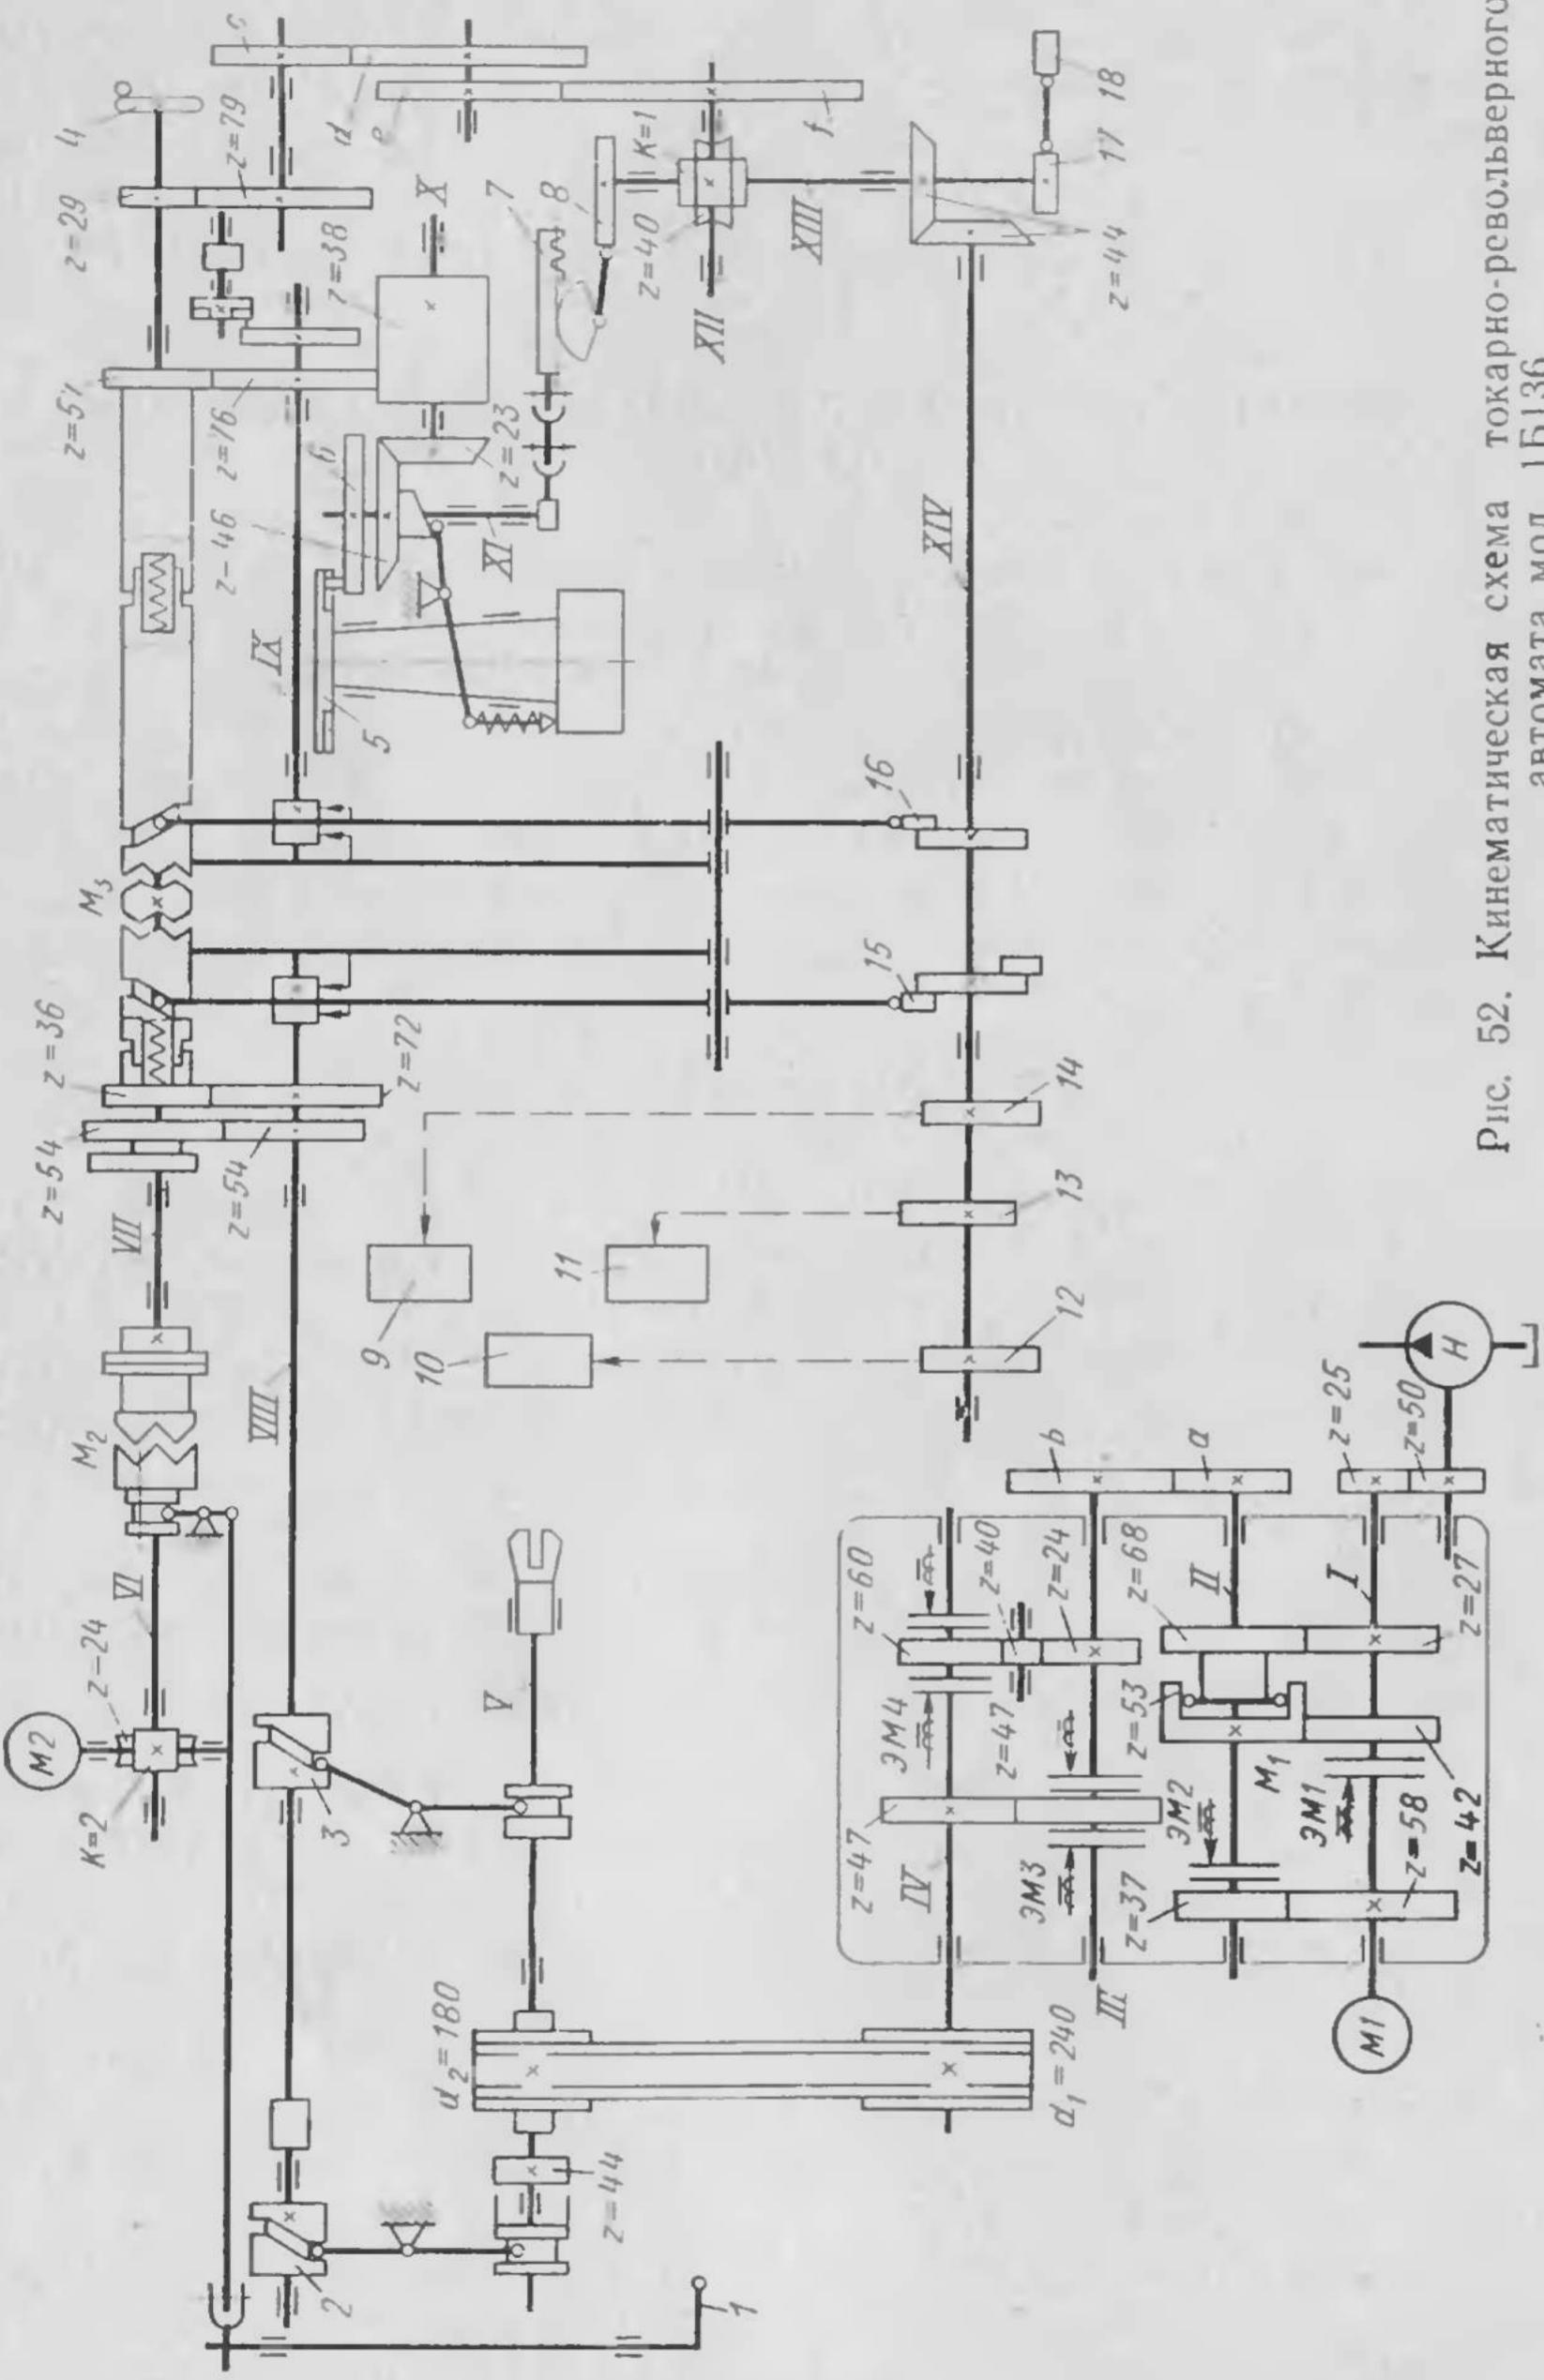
Кинематическая схема токарно-револьверного автомата мод. 1Б136
